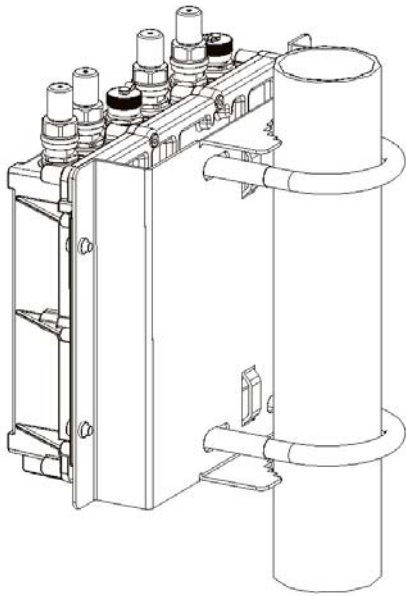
BAT450-F Masthalterungsset mit beigelegten Rundstahlbügeln
